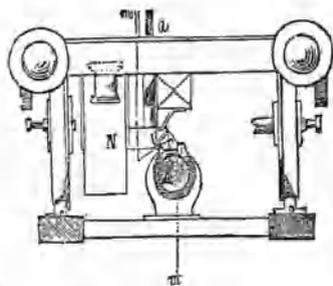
º Corte perpendicular al tubo y vista del frente del carro, después del paso del pistón viajero.
